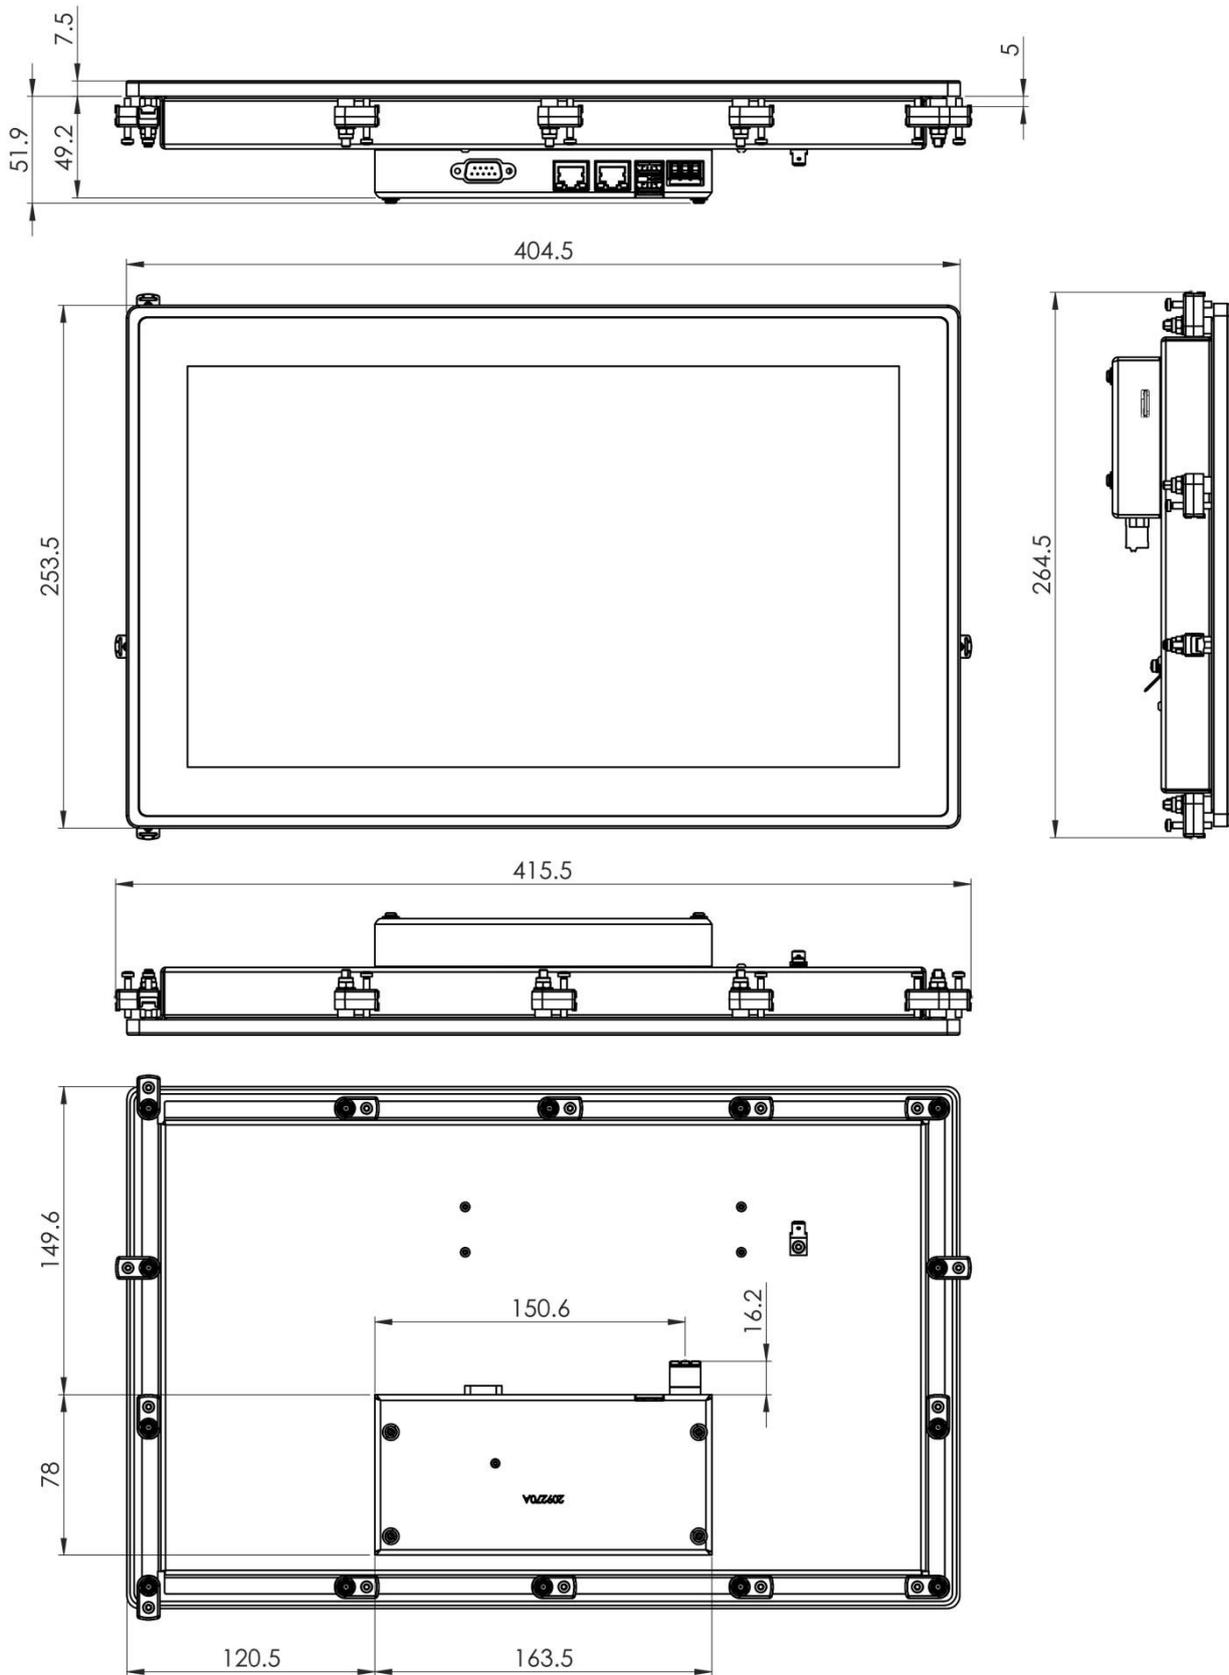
WP-156g 44-12x0 Montage-Ausschnitt
